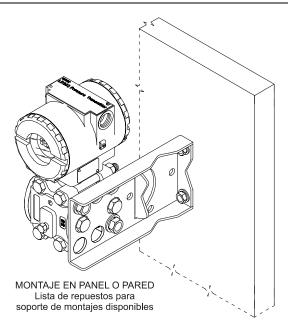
Diseño de Montaje del LD301 en Panel ó Pared
